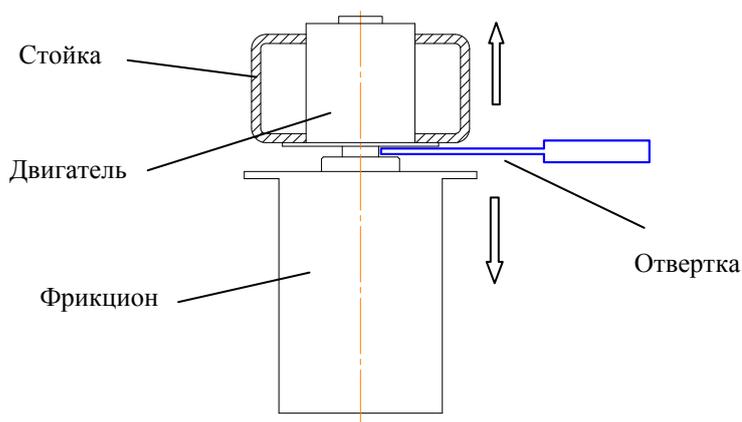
Снятие фрикциона с вала двигателя.
